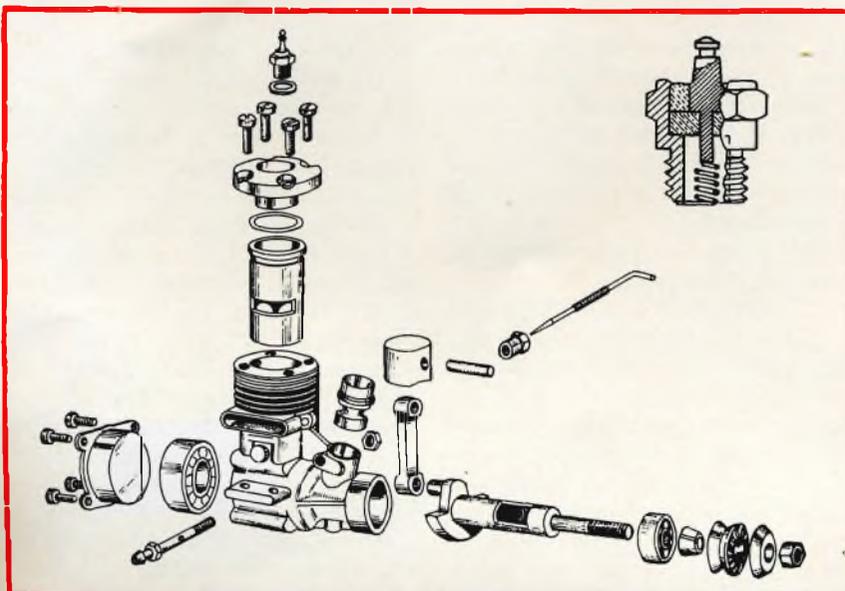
Disegno esploso di tutte le parti che compongono un motore a incandescenza o Glow plug.
